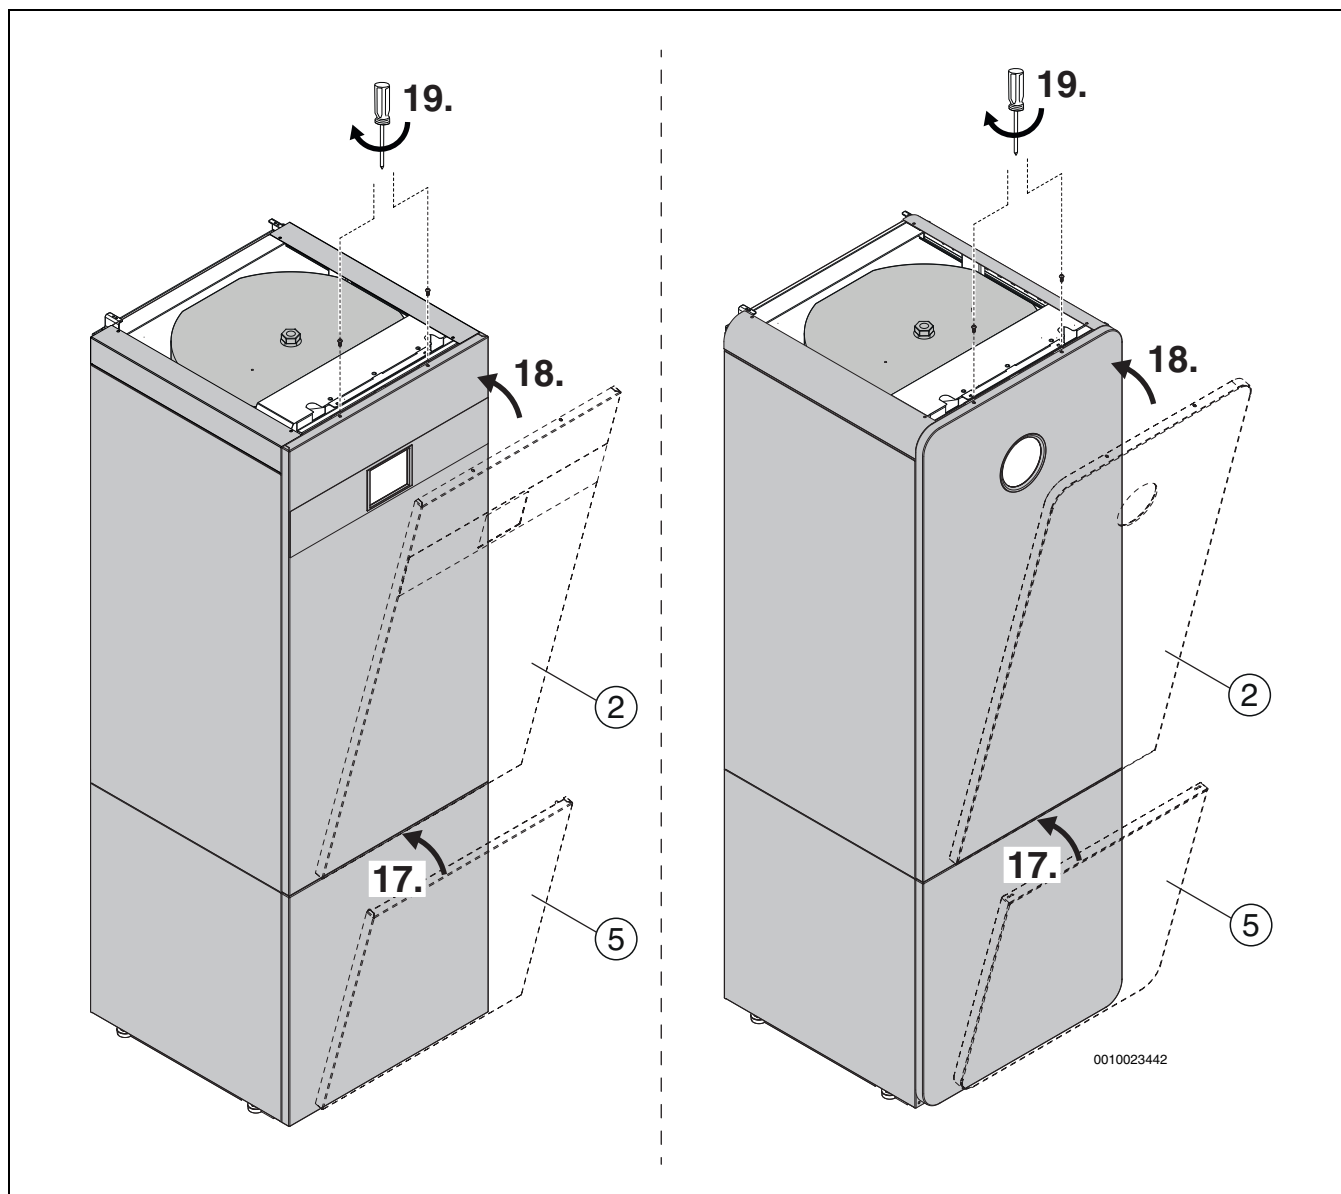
Montering af forvægge med firkantet eller rund afdækning
